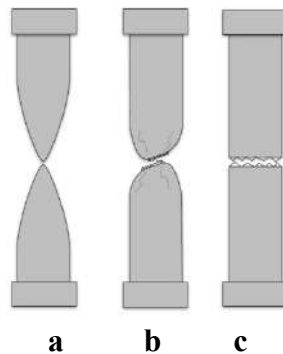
Tipos de fractura: (a) fractura dúctil, (b) fractura mixta, (c) fractura frágil [6]
